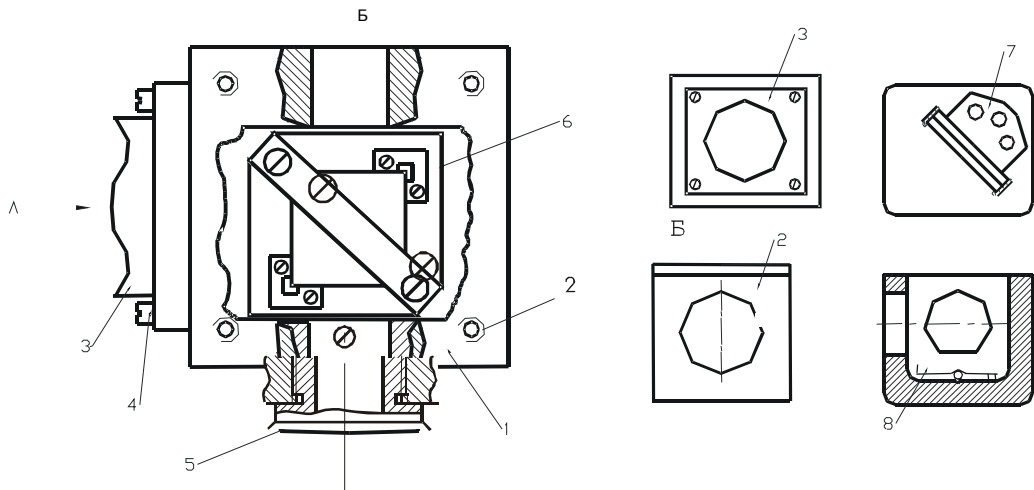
Корпус у формі куба: 1 – корпус; 2 – отвір для кріплення кришки корпусу; 3 – тубусний фланцевий елемент конструкції; 4 – гвинти, що кріплять фланець; 5 – тубусний різьбовий елемент (об'єктив, конденсор); 6 – призмовий блок; 7 – дзеркальний блок; 8 – плато
